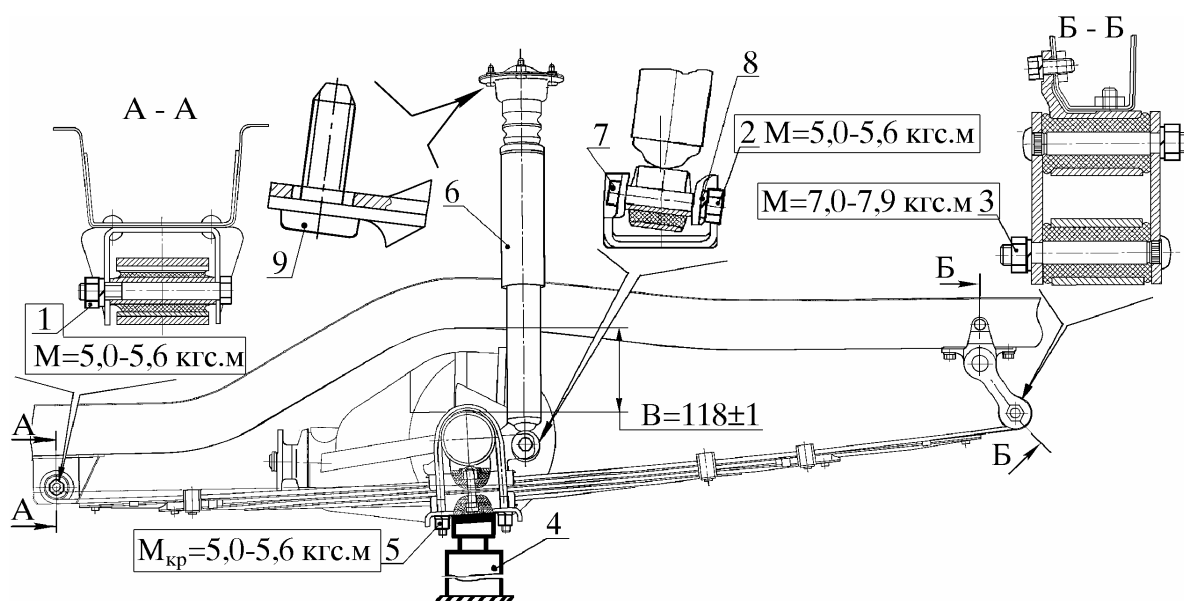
Установка амортизатора и затяжка гаек крепления рессоры:
